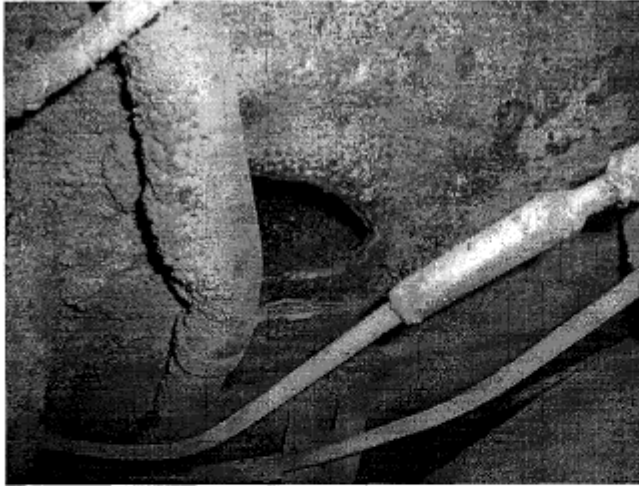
всасывающий патрубок, прогар металлоконструкции
